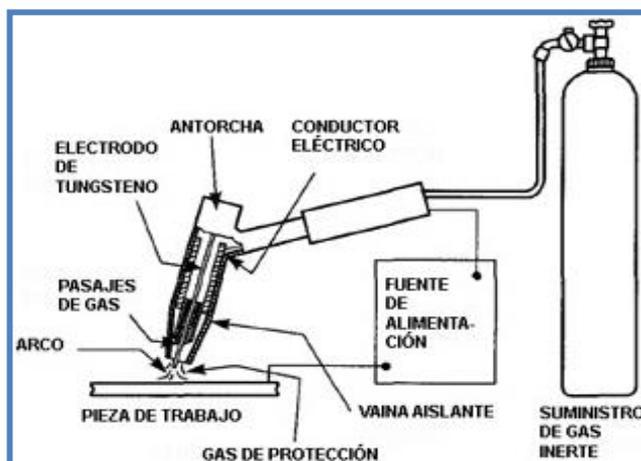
ESQUEMA GENERAL DEL EQUIPO DE SOLDADURA
